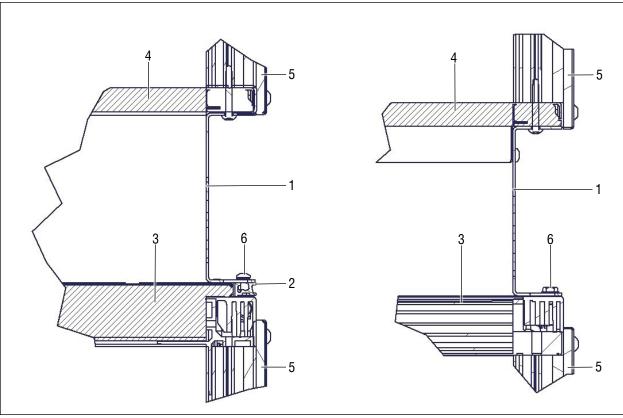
Disposition des appareils groupe de toit avec profil de cadre d'appareil (à gauche) et sans profil de cadre d'appareil (à droite)
